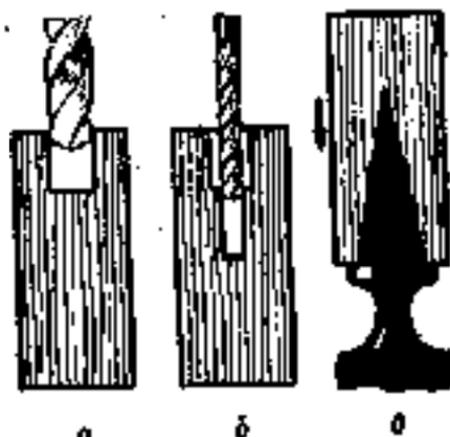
Насадка заготовки на хвостовик квадратного сечения с предварительным сверлением:
